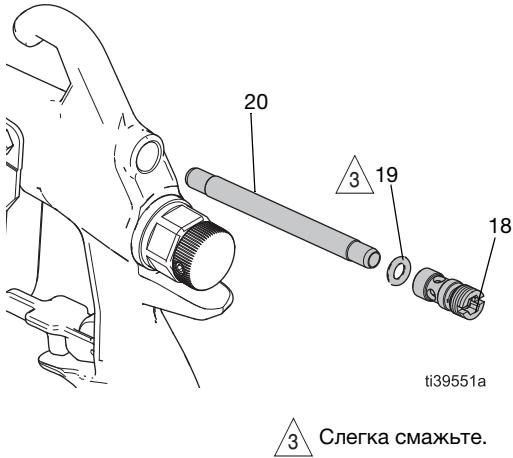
Направляющая клапана регулировки ширины факела в сборе
